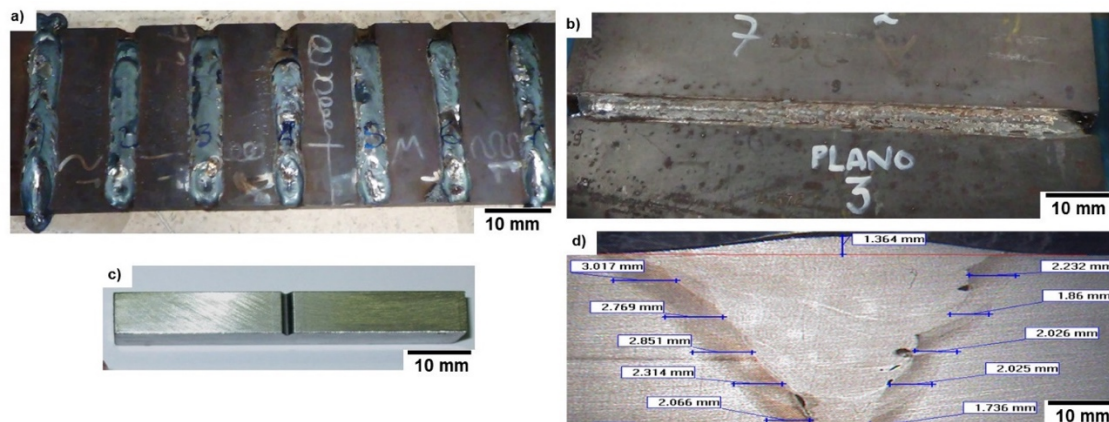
(a) Juntas soldadas a tope para pruebas de impacto; (b) juntas robóticas GMAW para pruebas de tensión; (c) espécimen tipo Charpy y (d) probeta para evaluación de dureza Vickers y la microestructura [12].
